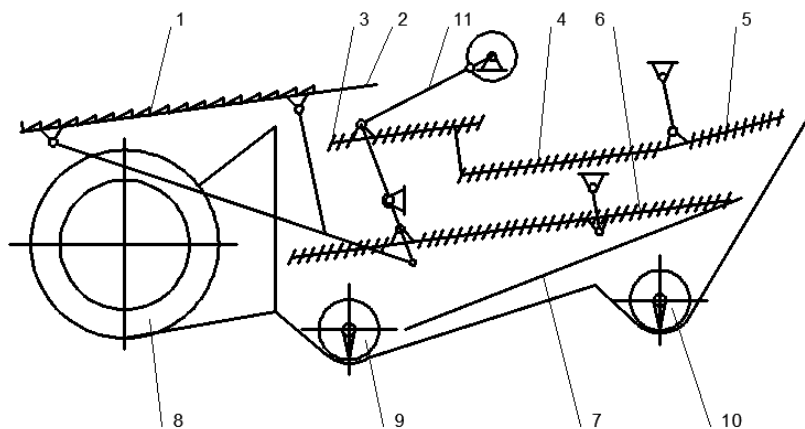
Схема очистки зерноуборочного комбайна КЗС-10К:
